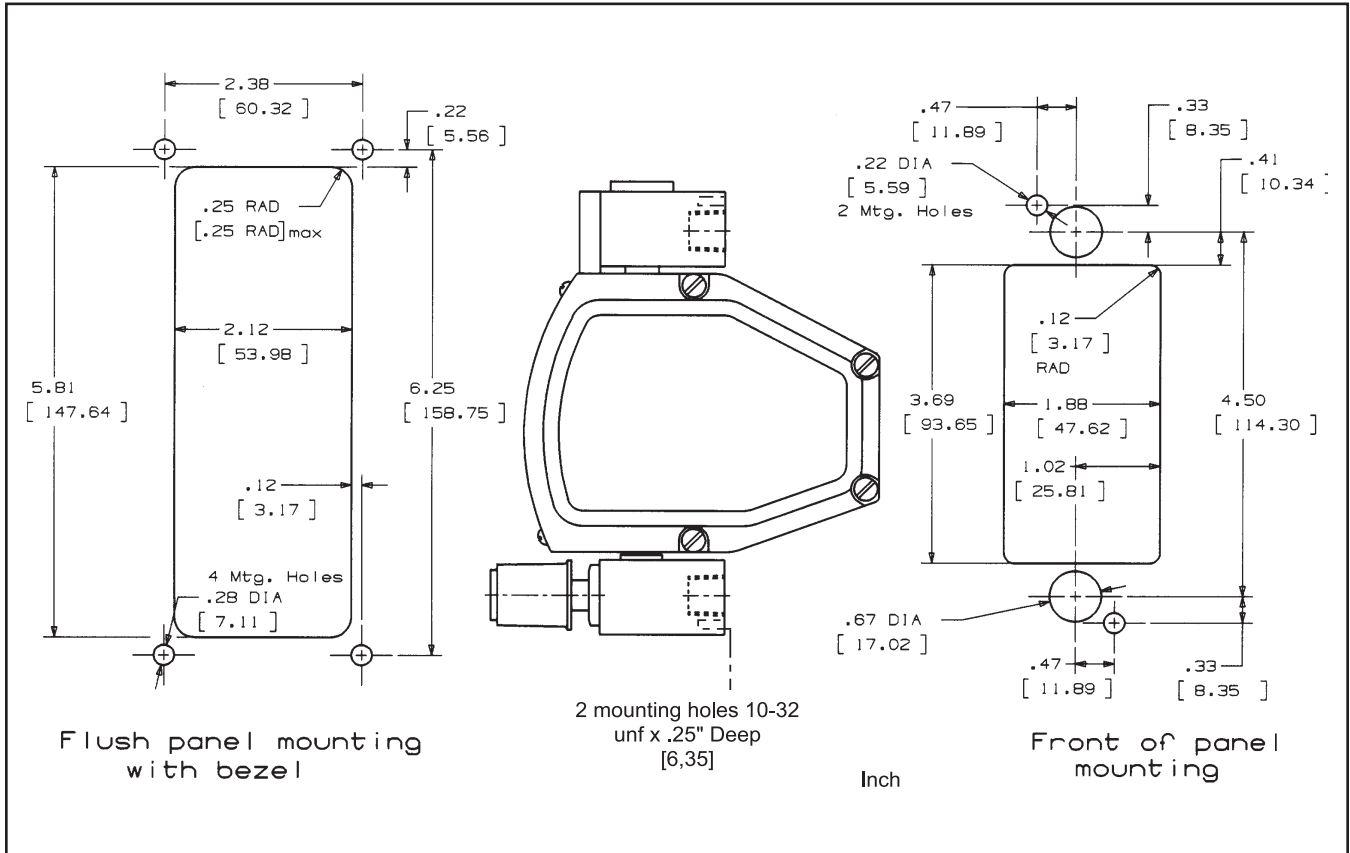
Dimensions pour le montage sur panneau MT3750C
